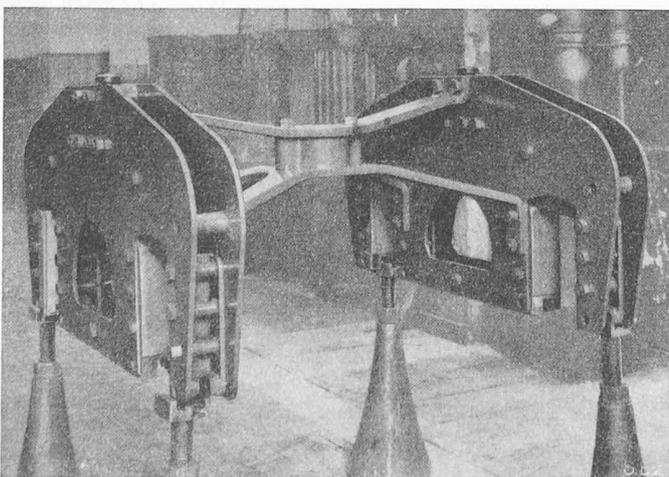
Drehgestellrahmen für die beiden Laufachsen
